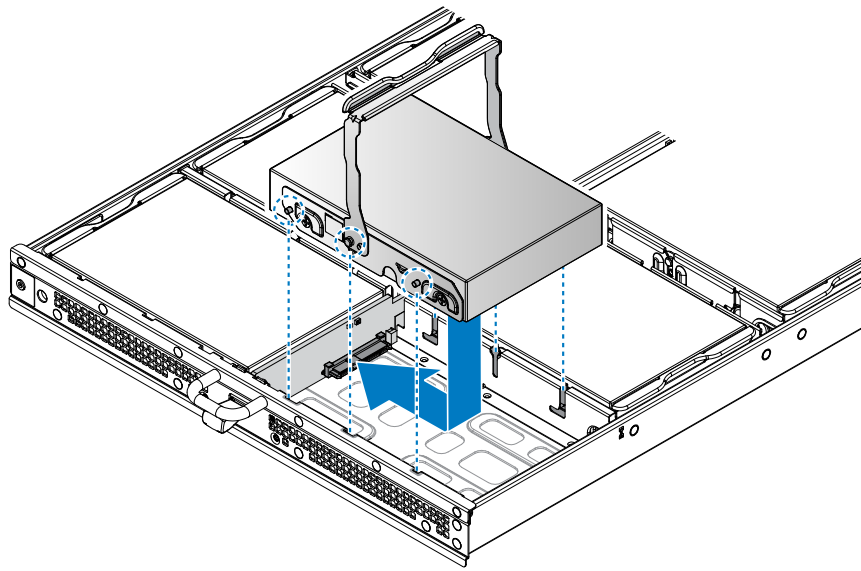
Installation de l'assemblage de disque dur de 3,5 pouces
